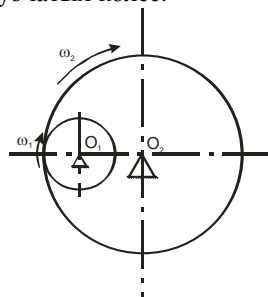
Зубчатый механизм с внутренним зацеплением
